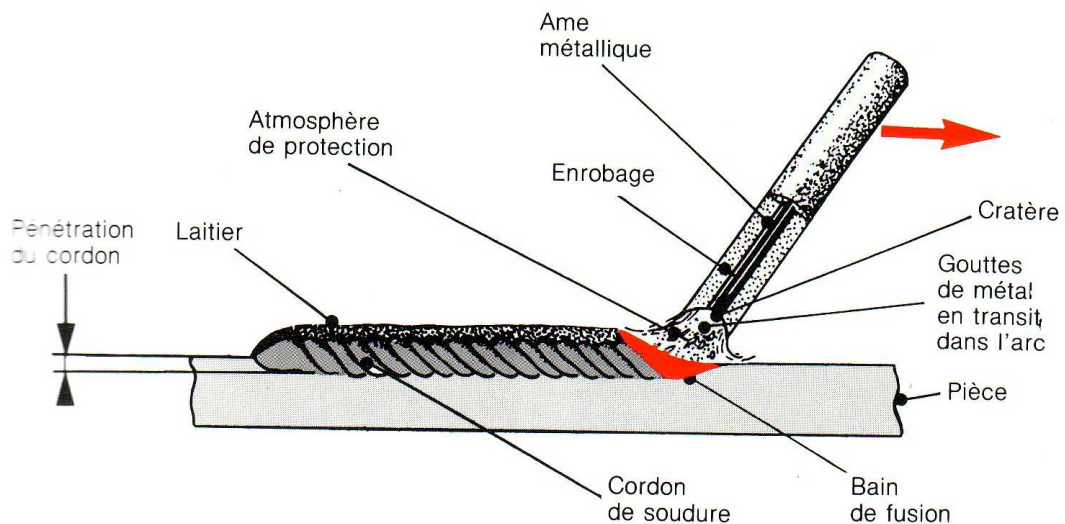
Principe de la soudure à l'arc électrique
